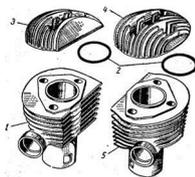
Цилиндры и головки цилиндров двигателя Ява-350:
